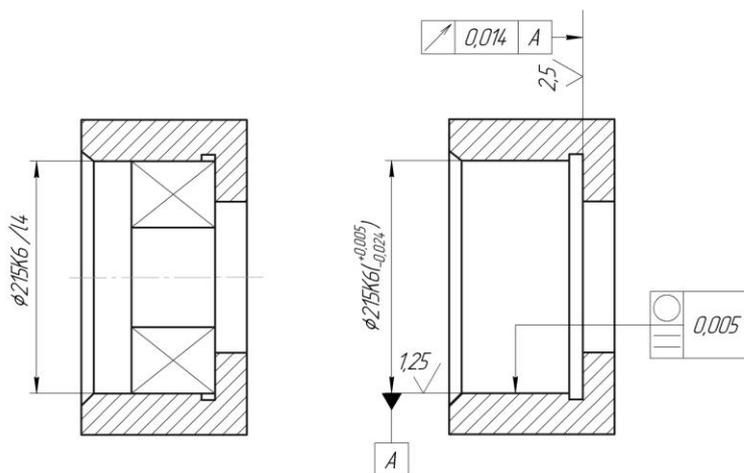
Ескіз посадки зовнішнього кільця підшипника в корпусі
